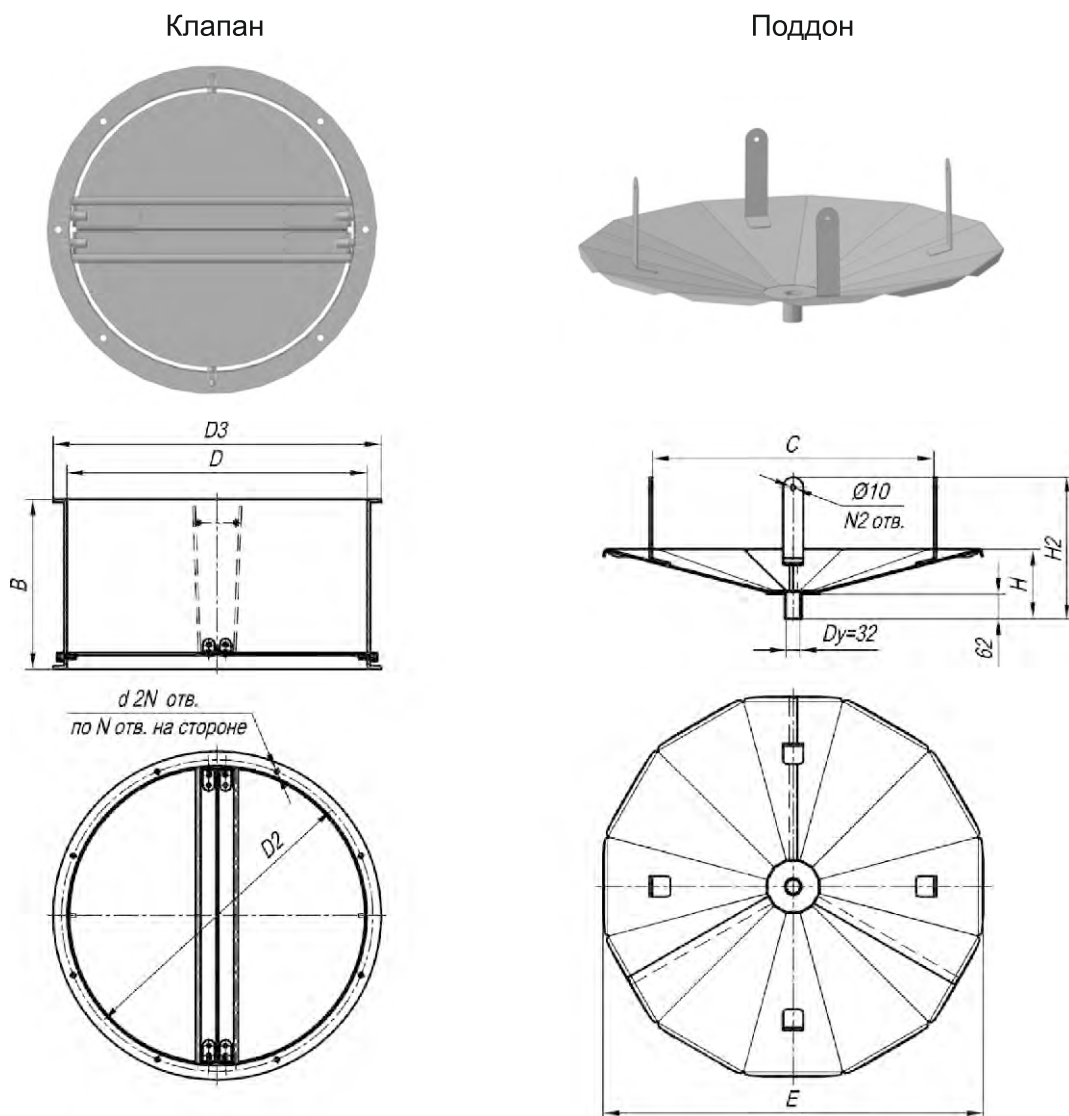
Габаритные и присоединительные размеры клапанов, поддонов для крышных вентиляторов.
